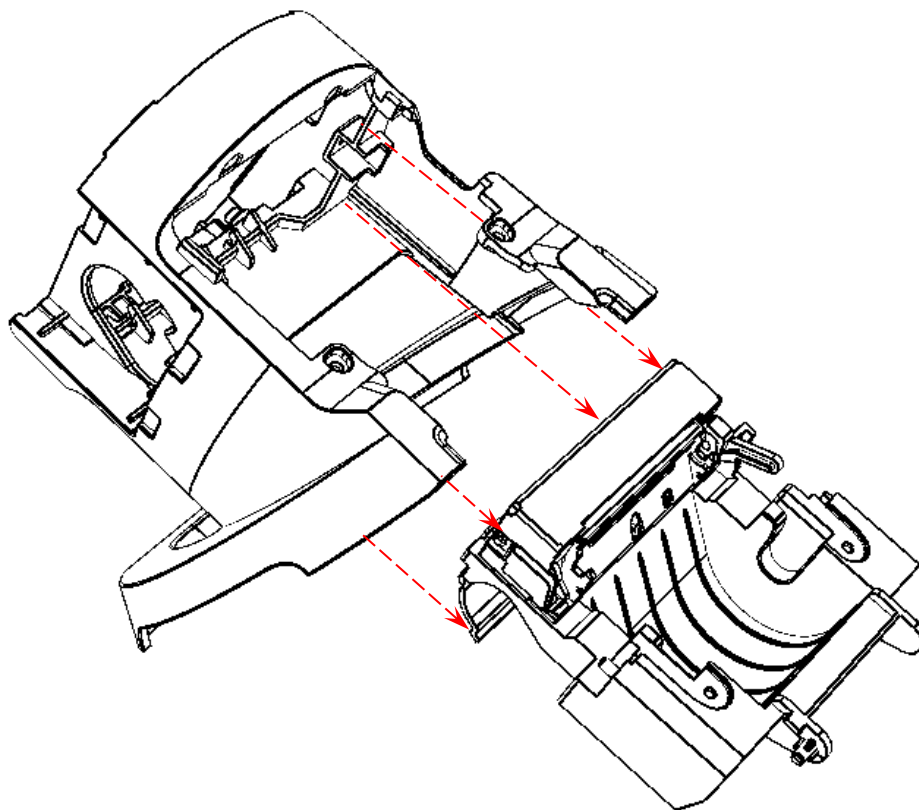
Извлечение лотка для ЧЛ с ТПМ из стойки
